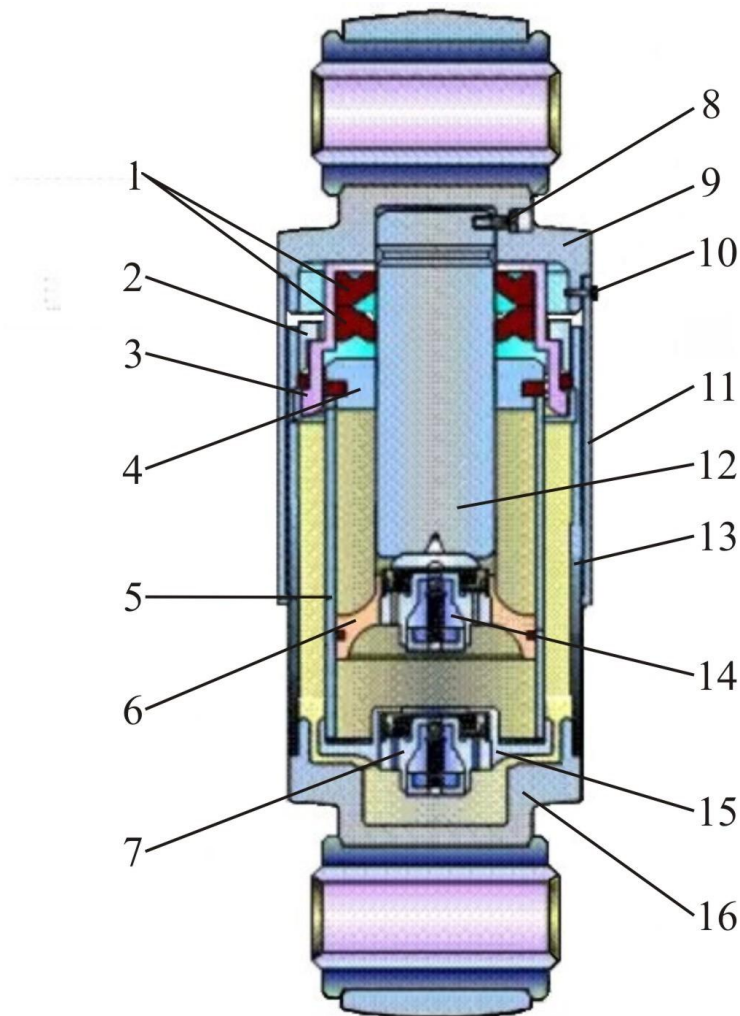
Загальний вигляд гідравлічного гасника коливань: 1 - сальники; 2 - гайка; 3 - обойма; 4 - напрямна букса; 5 - циліндр; 6 - поршень; 7 - клапан; 8 - гвинт; 9 - головка; 10 - болт; 11 - захисний кожух; 12 - шток; 13 - корпус; 14 - клапан; 15 - корпус; 16 – головка.
